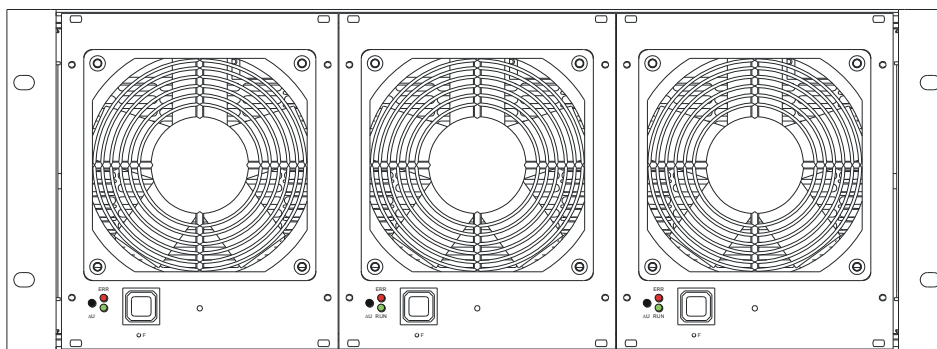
Frontansicht eines voll bestückten Baugruppenträgers M 3421
